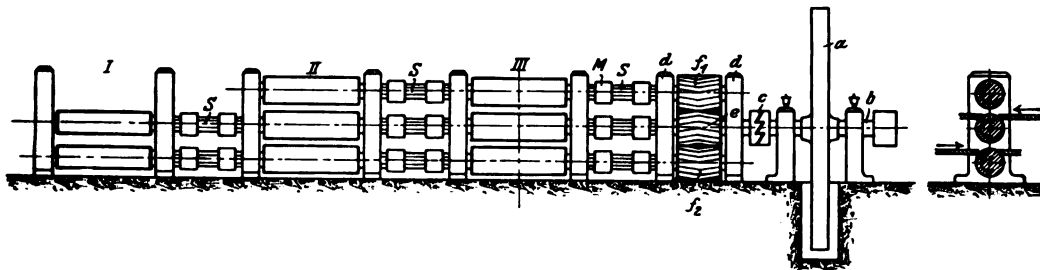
Schema einer Walzenstraße; a Schwungrad, b Welle mit Antrieb, c Kupplung, d Lagerböcke, e Kammwalze, f Kammräder, M Kupplungsmuffe, S Kupplungsstange.
